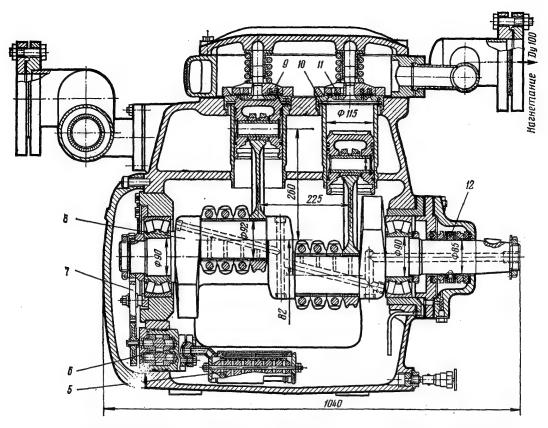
Бескрейцкопфный непрямоточный VV-образный одноступенчатый компрессор П220 1— блок-картер; 2— гильза цилиндра; 3— поршень с кольцами; 4— шатун; 5— заборный масляный фильтр; вовесами; 9— ложная крышка; 10— всасывающий клапан; 11— нагнетательный клапан; 12— сальник уп-
